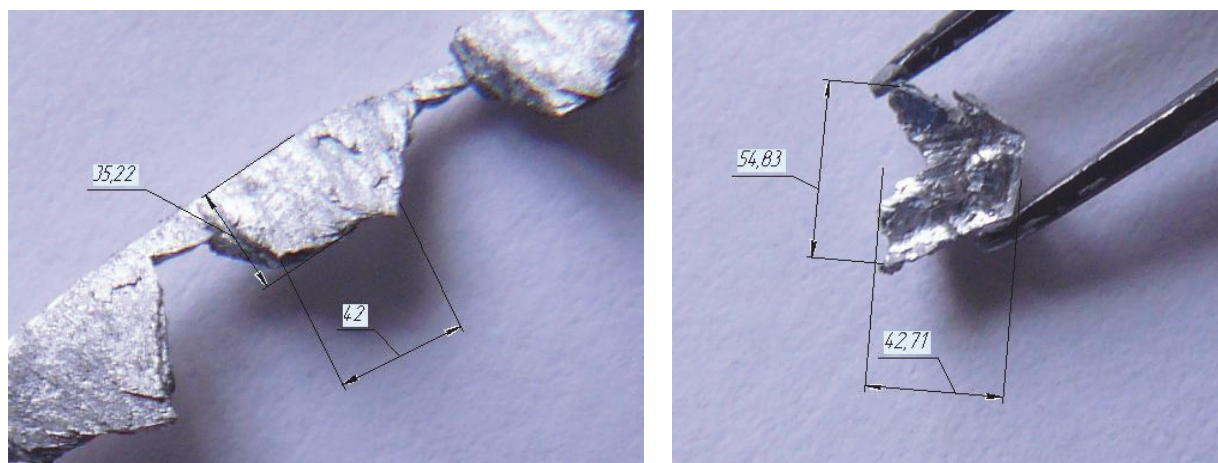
Алюминиевая стружка, полученная зубчатым (слева) и гладким (справа) режущими элементами
